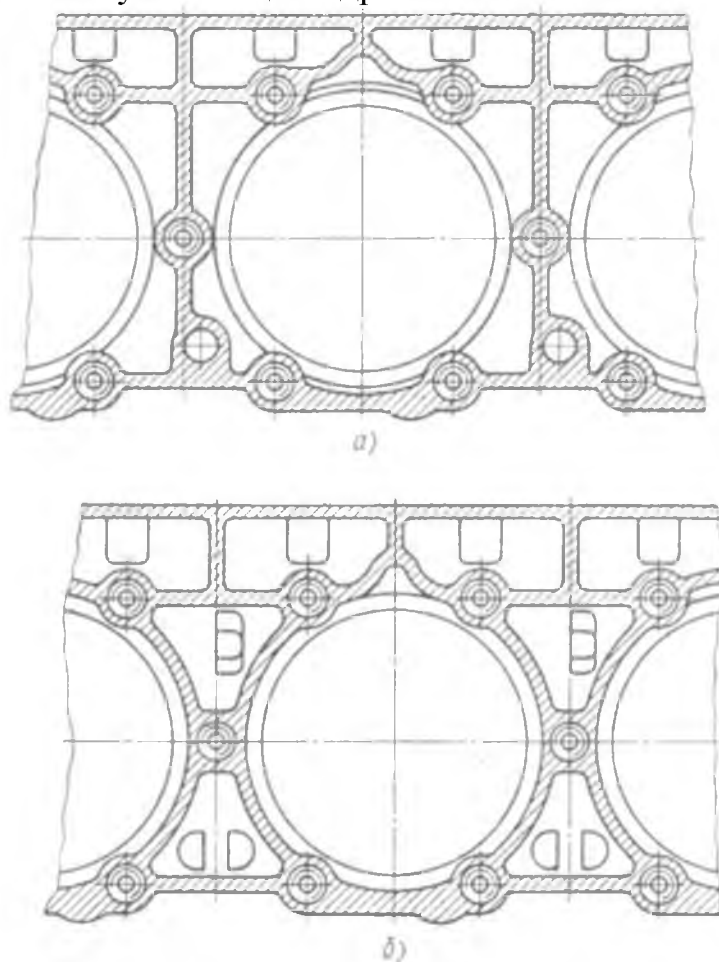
Конструкції циліндрової частини блоку: а - вихідна; б - змінена
